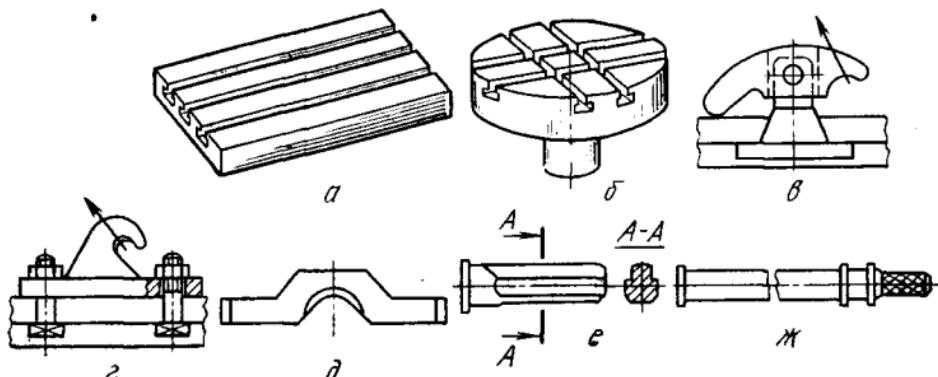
Вспомогательные приспособления для строповки станков и узлов оборудования:
